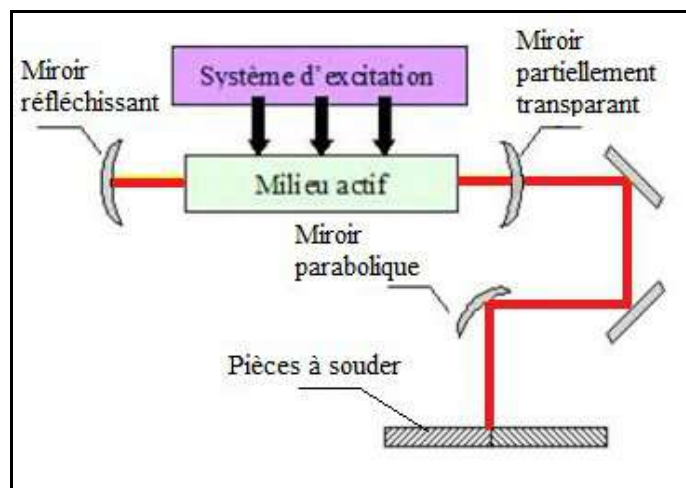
Principe de soudage laser CO₂ [34].
